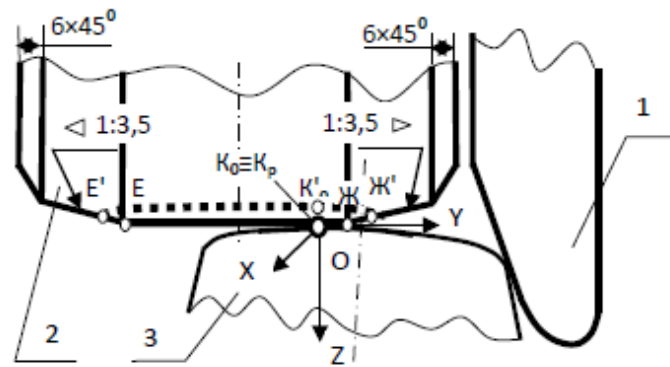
Поперечные профили поверхностей катания колес колесного блока
